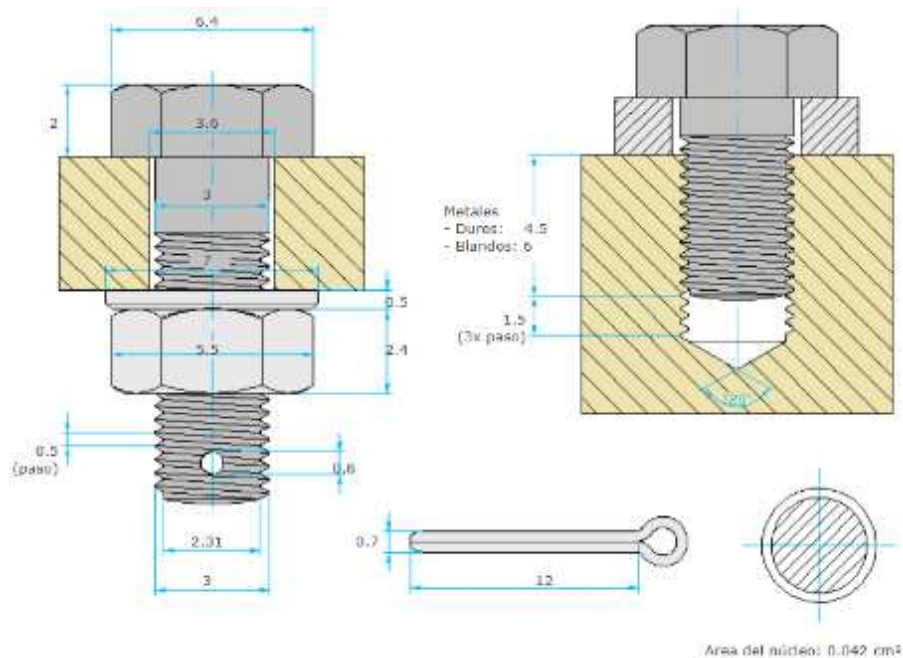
Esquema del tornillo de rosca métrica ISO DIN 13 Fuente: [23]
